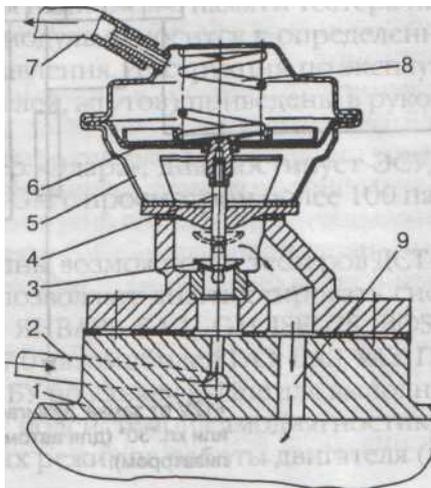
Клапан рециркуляции ОГ: 1 - ресивер; 2 - трубка подвода ОГ; 3 - клапан; 4 - шток; 5 - клапан рециркуляции; 6 - диаграмма; 7 - шланг для подвода разрежения; 8 - пружина; 9 - канал для прохода ОГ в ресивер
